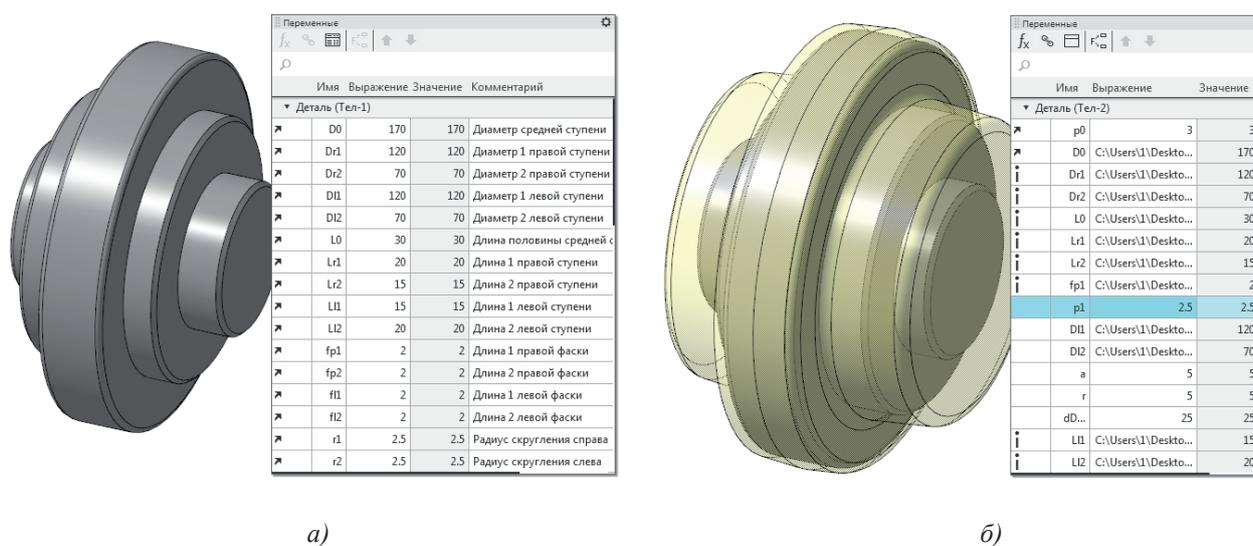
Деталь в форме диска (а) и ассоциативно связанная с ней заготовка (б)
